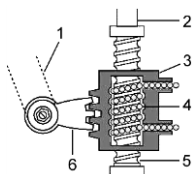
Рулевой механизм с шариковой гайкой: 1 – сошка; 2 – вал рулевого колеса; 3 – гайка рулевого механизма с рейкой; 4 – рециркулирующие шарики; 5 – винт рулевого механизма; 6 – зубчатый сектор.
